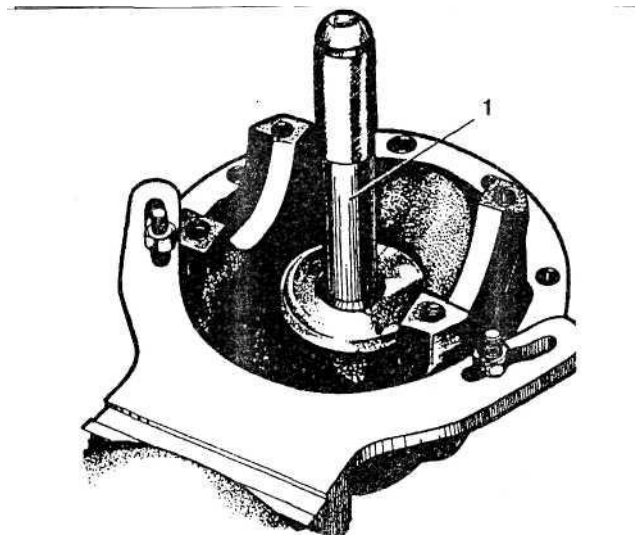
Установка с помощью оправки наружного кольца заднего подшипника ведущей шестерни: 1 - оправка А. 70171
